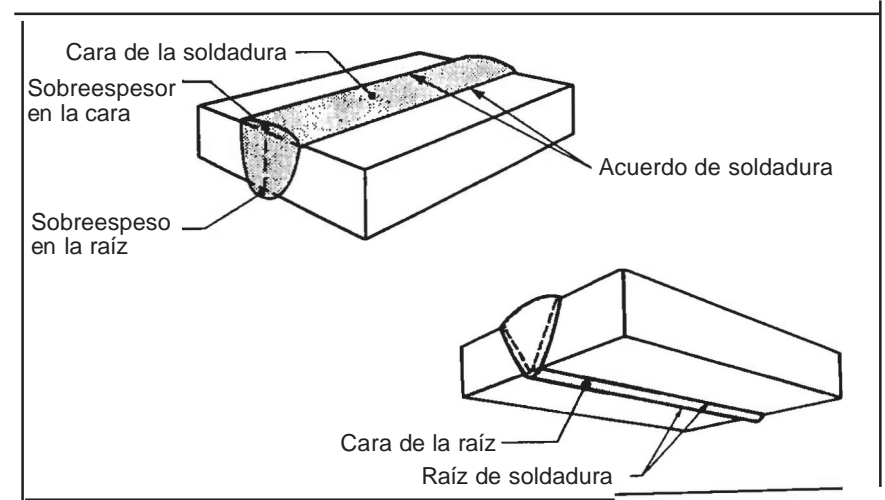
CARA Y RAÍZ DE UNA SOLDADURA
